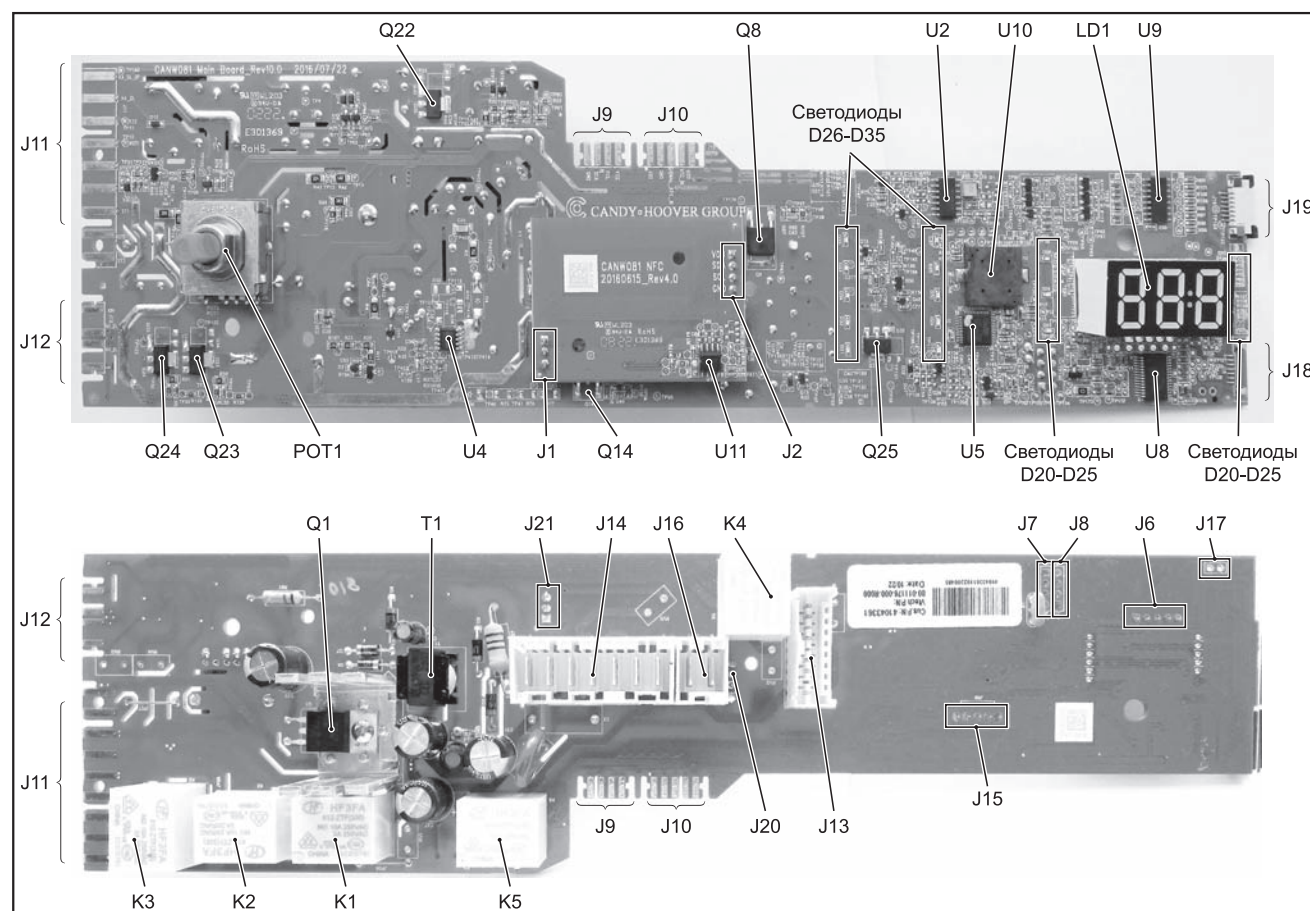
Внешний вид ЭМ 49043445 и расположение на нем основных компонентов, где: а — вид сверху; б — вид с обратной стороны
